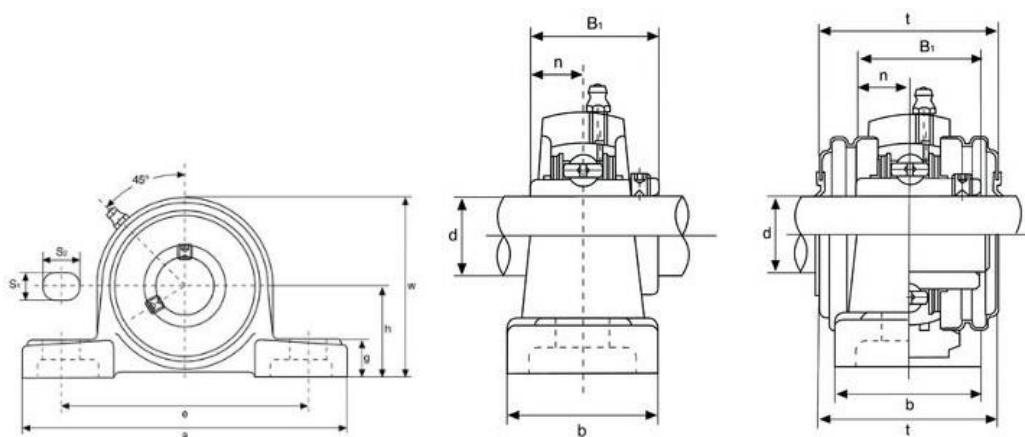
Корпусной, чугунный подшипниковый узел на лапах серии УСР-2 с удлиненным внутренним кольцом
